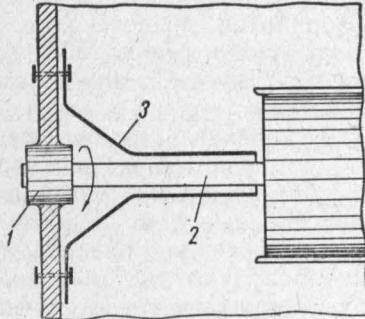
Защита вращающегося вала неподвижным кожухом-втулкой:
